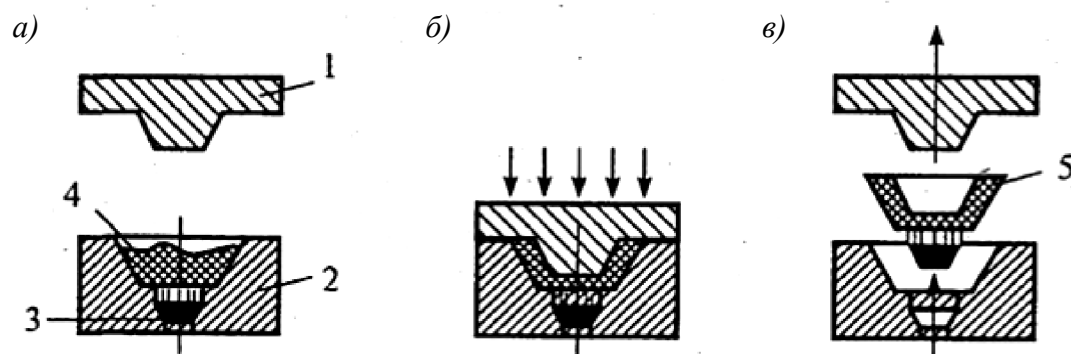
Схема изготовления изделий прессованием: а – загрузка шихты в пресс-форму; б – прессование; в – извлечение изделия; 1 – пунсон; 2 – матрица; 3 – выталкиватель; 4 – пресс-материал; 5 – готовое изделие
